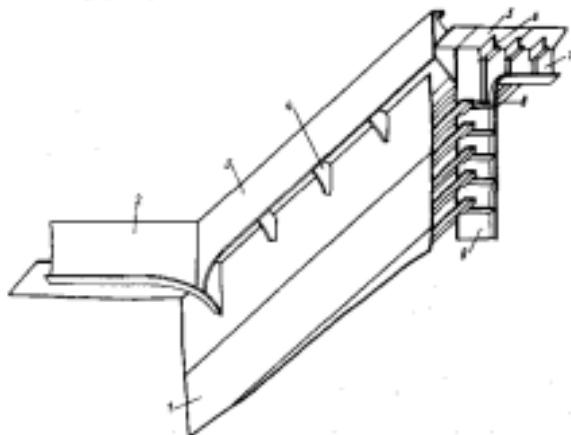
Продольный переборка двойного борта, усиленные карлингсом:
